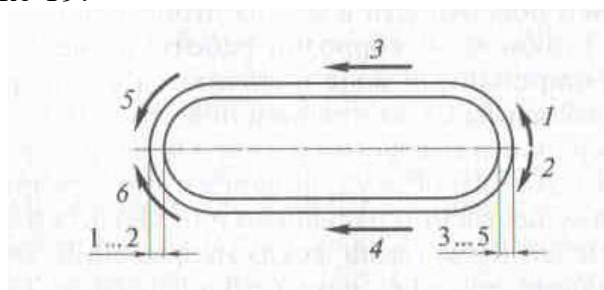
Последовательность выполнения сварного соединения при варке заплатки
